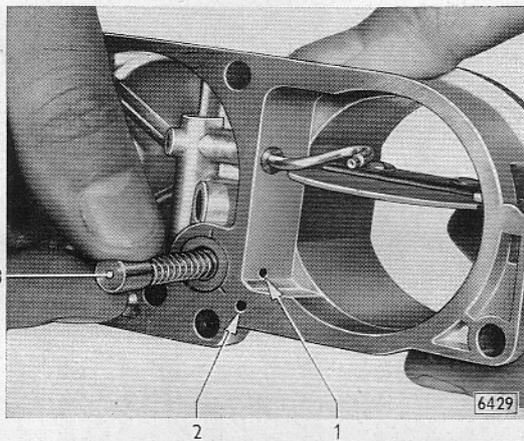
Unterdruckkolben mit Kolbenstange auf Freigängigkeit prüfen
